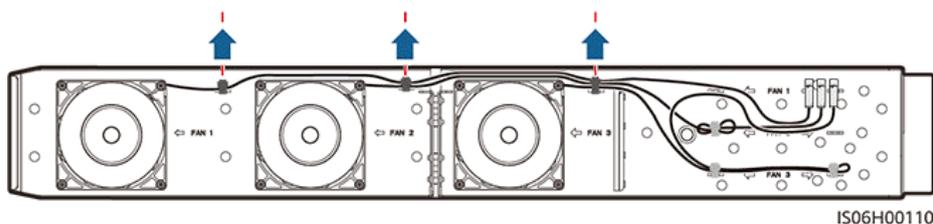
Extracción de la bandeja de ventiladores (2)
